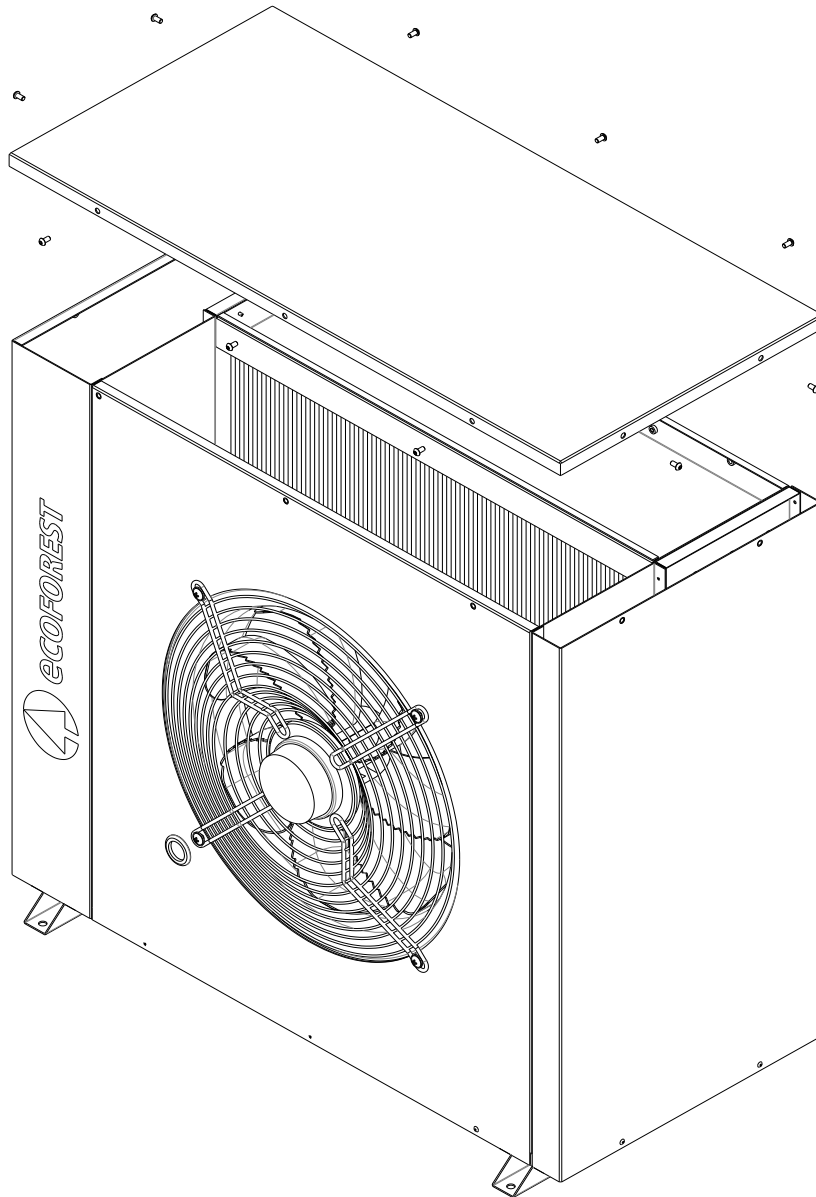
Desmontaje de la tapa superior de las unidades AU12.
